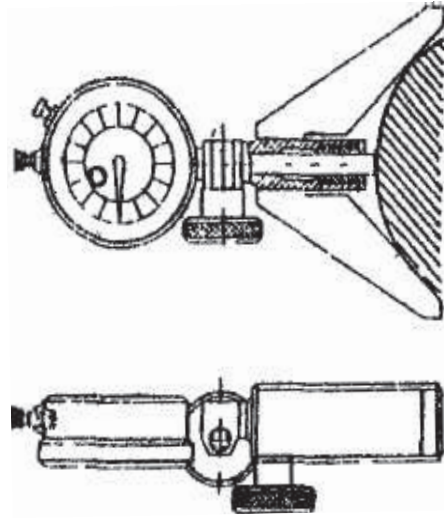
Схема установки индикатора на «0» перед установкой вылета резца по наезднику
